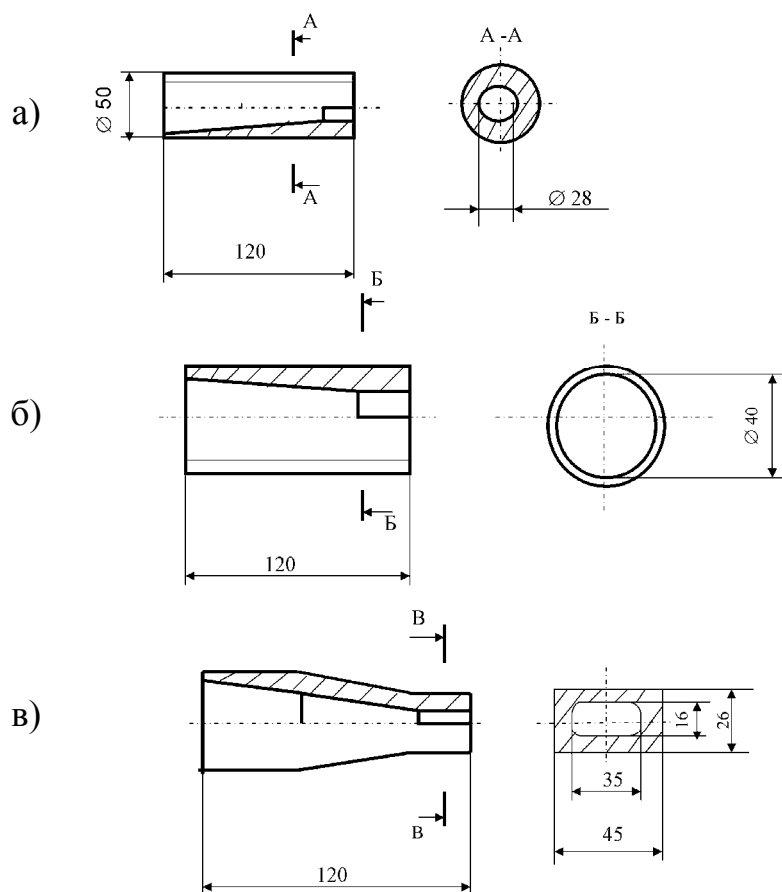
Варианты конструкции сопла для нанесения бетонных смесей:
